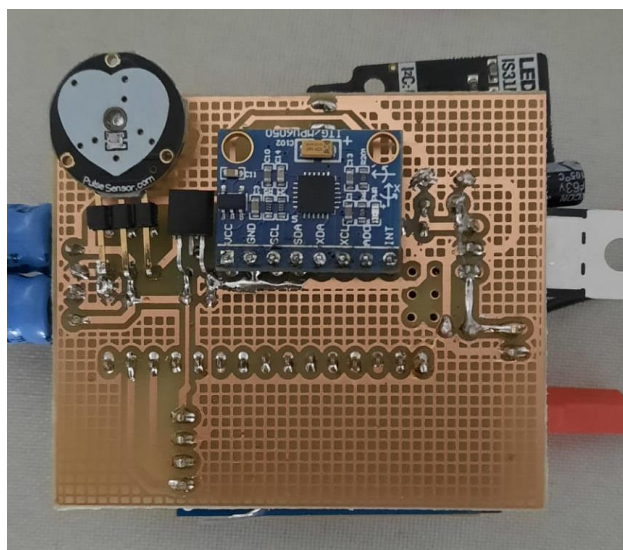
Vista real da parte inferior da PCB, com os sensores biométricos soldados
